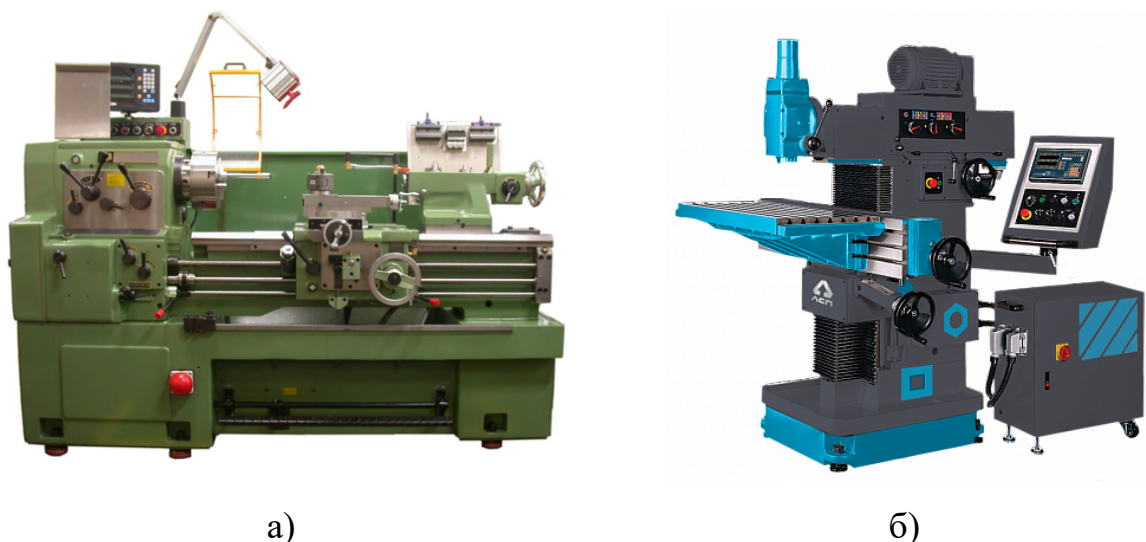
Металлорежущие станки: а) универсальный токарный станок СТ16К20; б) станок фрезерный JET 67Л35ПФ1 универсальный
